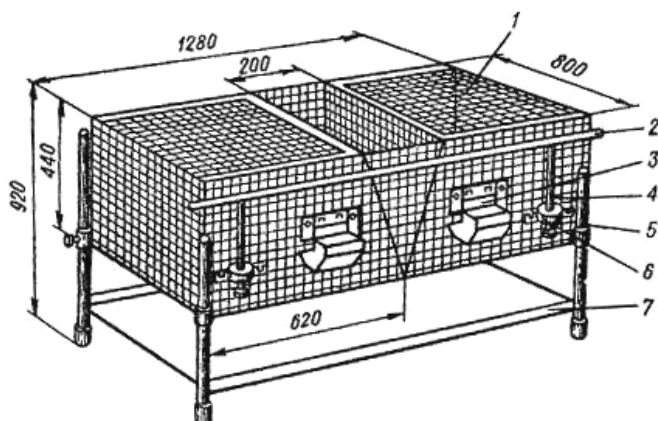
Клетка КСК-1: 1 – дверцы; 2 – коллекторная трубка; 3 – бункерная кормушка; 4 – гибкий шланг; 5 – стойка; 6 – поплавковая поилка; 7 – металлический поддон
